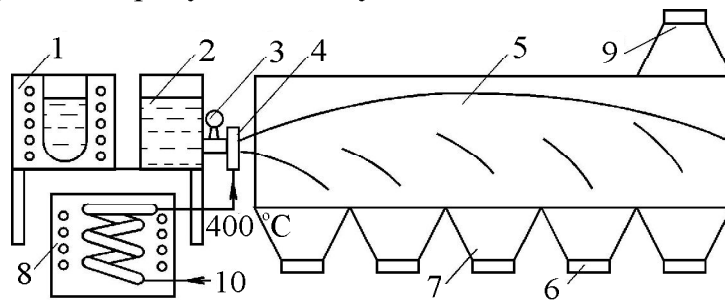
Установка для одержання порошку з індукційним плавленням металу і розпорошенням розплаву газом: 1 — піч; 2 — металоприймач; 3 — вентиль; 4 — форсунка; 5 — камера розпорошення; 6 — затвор; 7 — бункер; 8 — піч для підігріву повітря; 9 — вихід повітря; 10 — подача повітря
